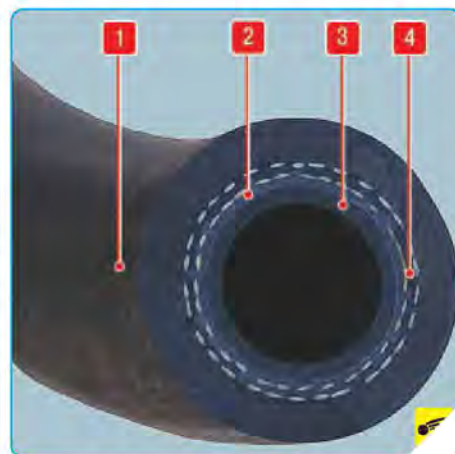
Конструкция шланга гибкой трубки: 1 – наружная защитная оболочка; 2 – пластмассовый герметизирующий слой; 3 – внутренний масляный слой; 4 – тканевый корд силового каркаса
